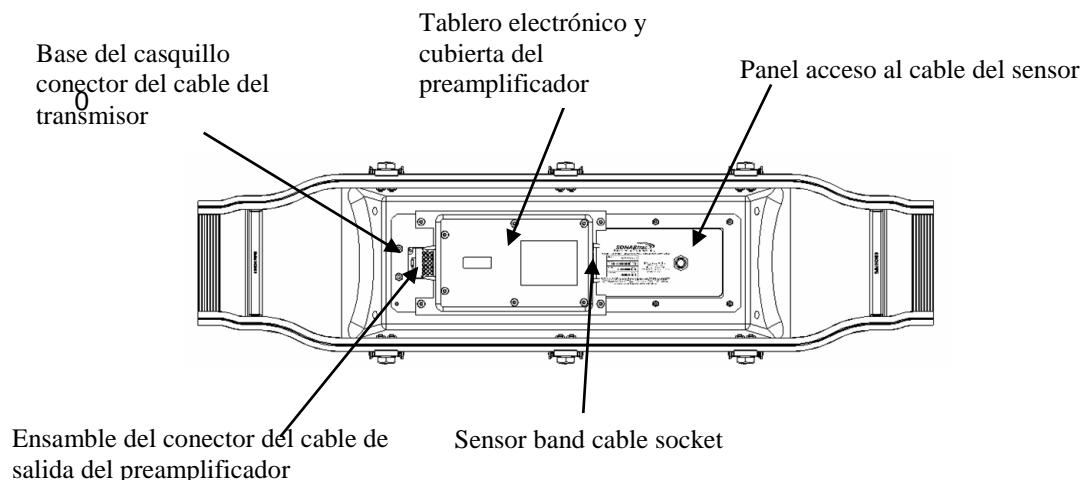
Vista Interior del Ensamble de la Cubierta Superior del Sensor
